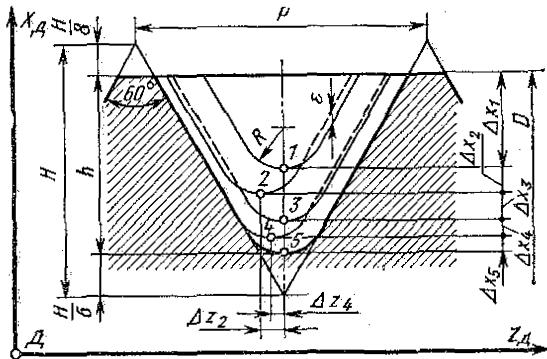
Схема нарезания резьбы М30 детали «вал»
